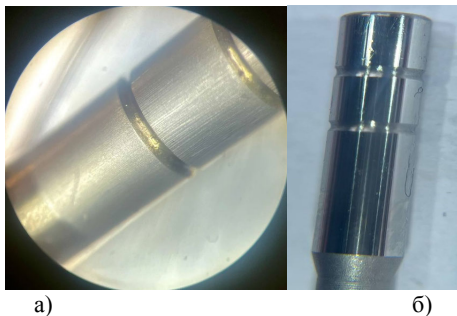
Торцевая поверхность штока управляющего клапана (мультипликатора) со следами изнашивания (а), торцевая поверхность нового штока управляющего клапана (б)
